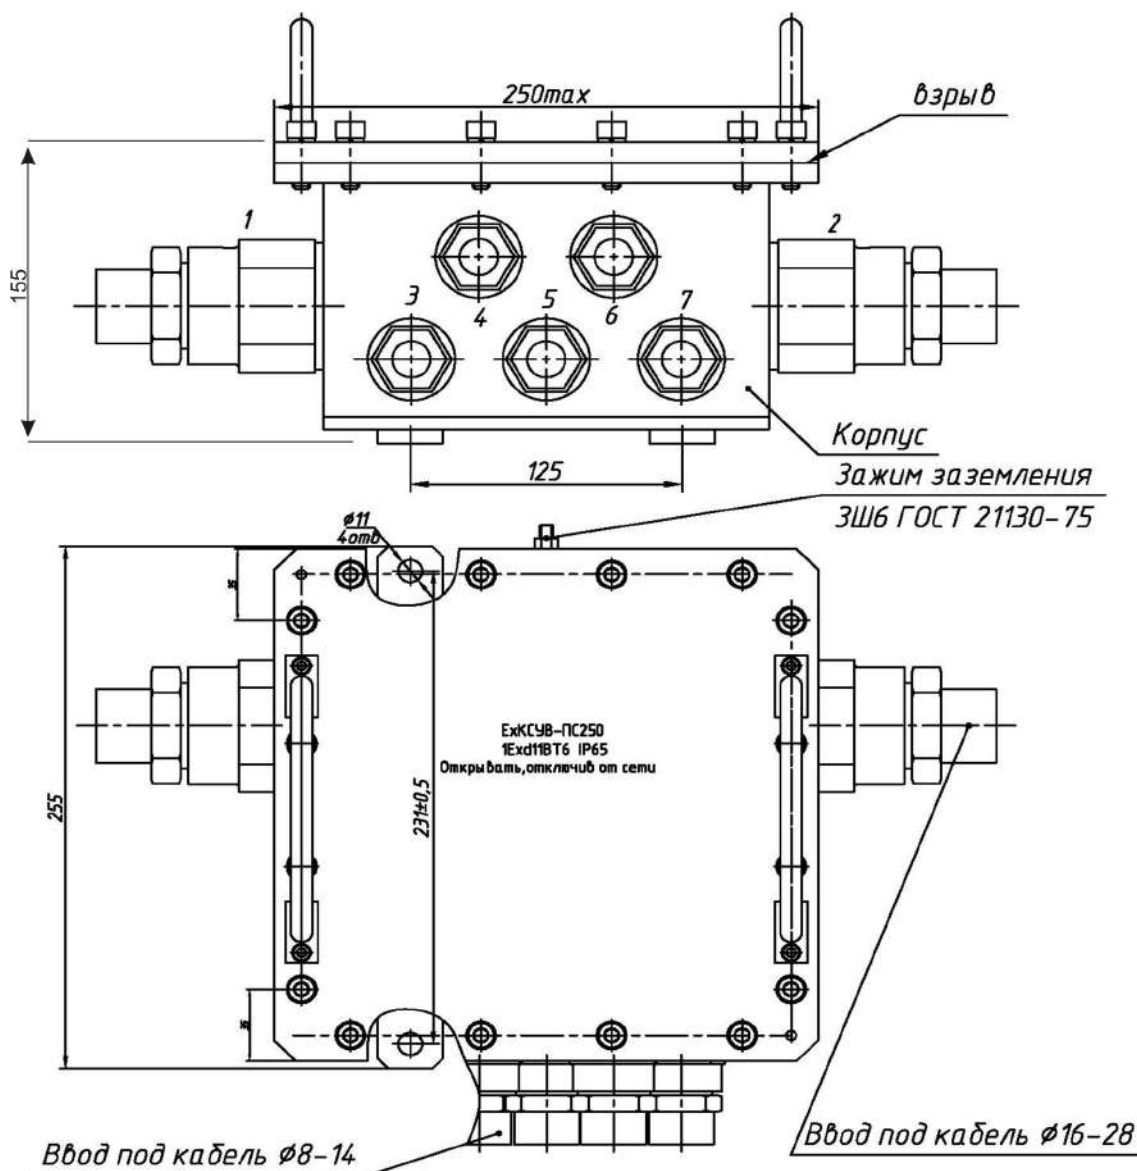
Габаритные, установочные и присоединительные размеры коробки ЕхКСУВ–ПС–250.
